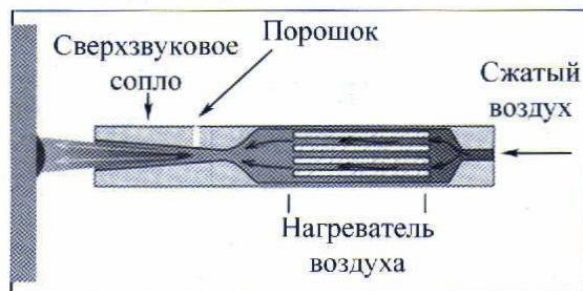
Схема установки ДИМЕТ, включающей нагреватель газа, открытый порошковый питатель, узел инъекции порошка в расширяющуюся часть сопла и сопло Лавала
